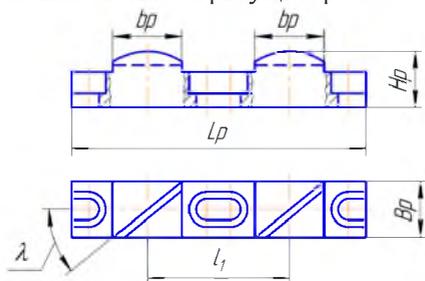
Конструкция резца-зуба развёртки со сдвоенными безвершинными зубьями
